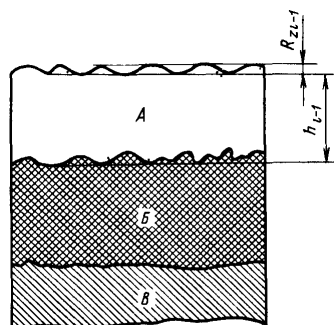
Схема поверхностного слоя после обработки наружной поверхности заготовки
